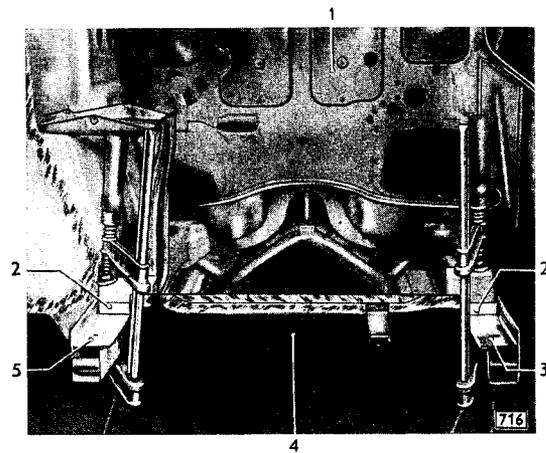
Vorderrahmenquerträger mit Obergurt in Einbaulage festgespannt
